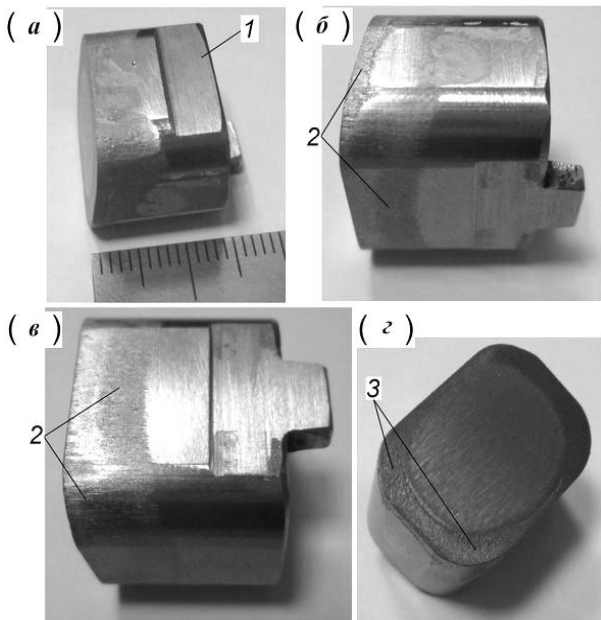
Участки износа штампового инструмента: 1 – посадочное место; 2 – боковая поверхность; 3 – рабочая (торцевая) поверхность
